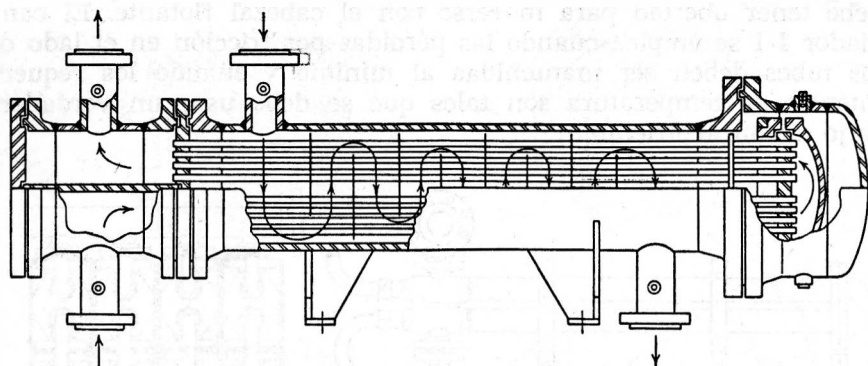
Cambiador uno-dos: carcasa de paso sencillo, tubos de dos pasos, haz de tubos removible. (Cortesía de Engineers and Fabricators, Inc.)
